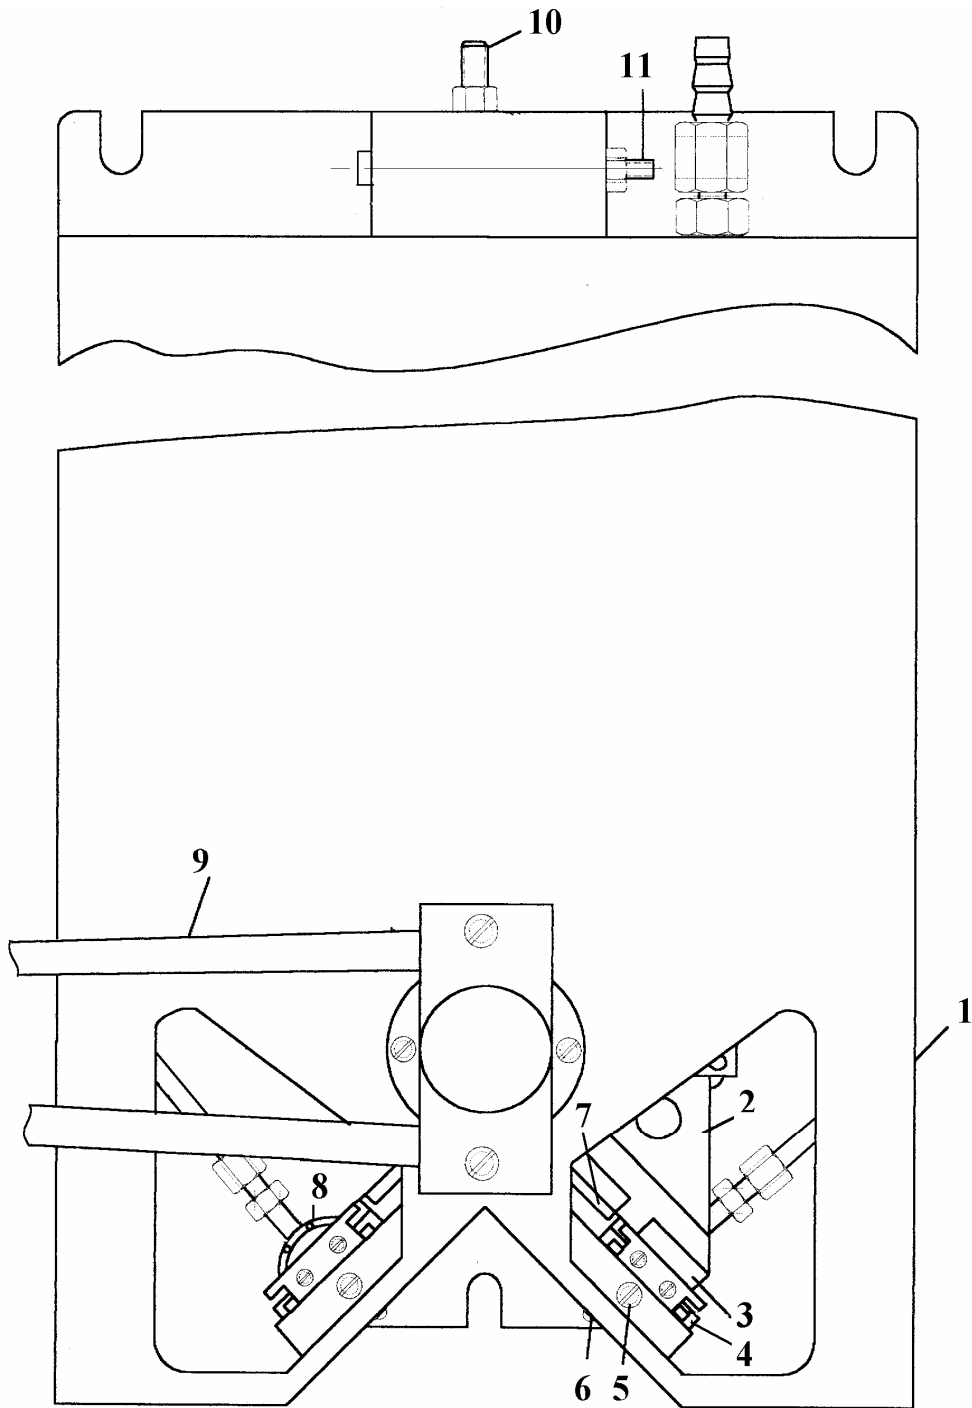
Макет робота с приводом колебательного типа: 1 – корпус робота; 2 – подвижный элемент исполнительного органа; 3 – постоянные магниты, 4 – постоянные магниты, управляемых упоров-фиксаторов (поз 2 на рис. 2.3); 5, 6, 10, 11 – регулировочные винты; 7 – постоянные магниты на упоре (поз. 3 на рис. 2.3); 8 – пневмоцилиндр; установленные на подвижном элементе исполнительного органа (поз.3 на рис. 2.3); 9 – исполнительный орган (механическая рука);
